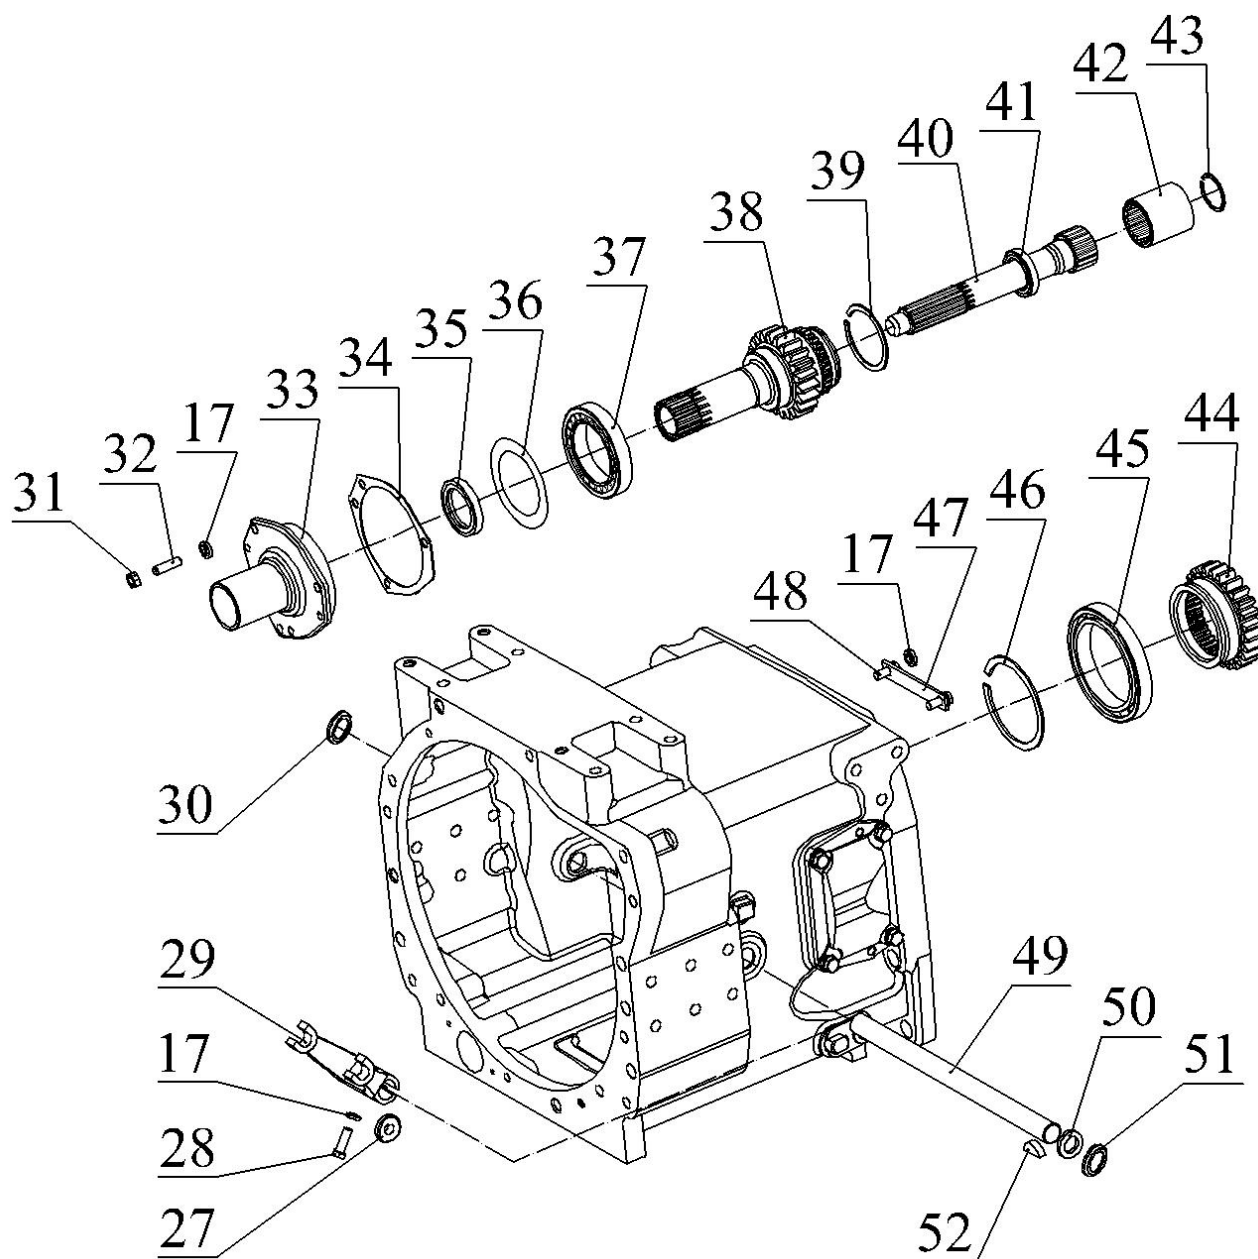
Корпус сцепления (лист 2 из 3)
